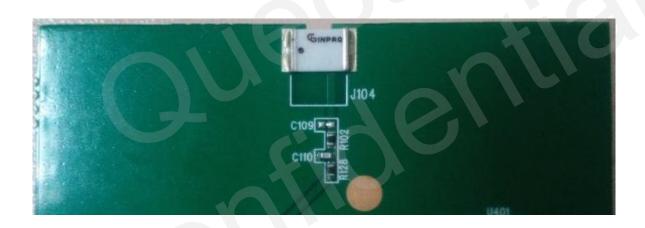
INPAQ 5036 Chip 天线在 M26 TE-A 上实物图
